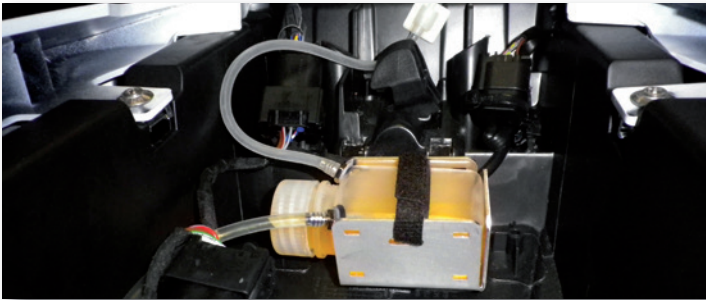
Belüftungsschlauch mit Kabelclip und Schlauchverbinder oberhalb des Ölstandes befestigt
